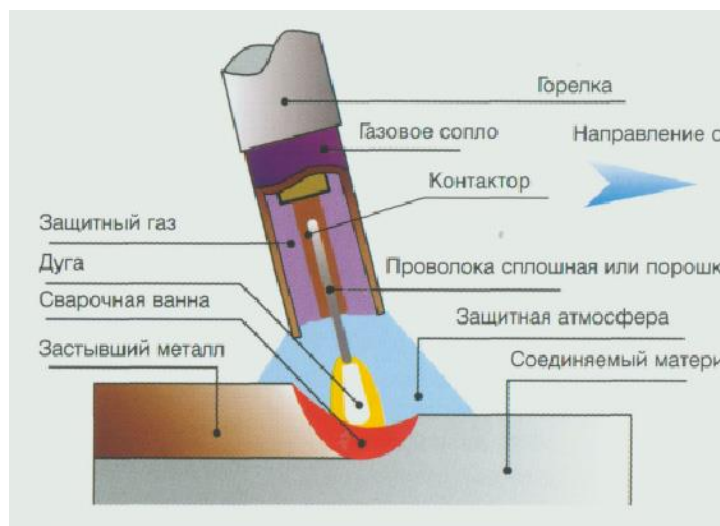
Механизированная сварка в среде защитного газа.
